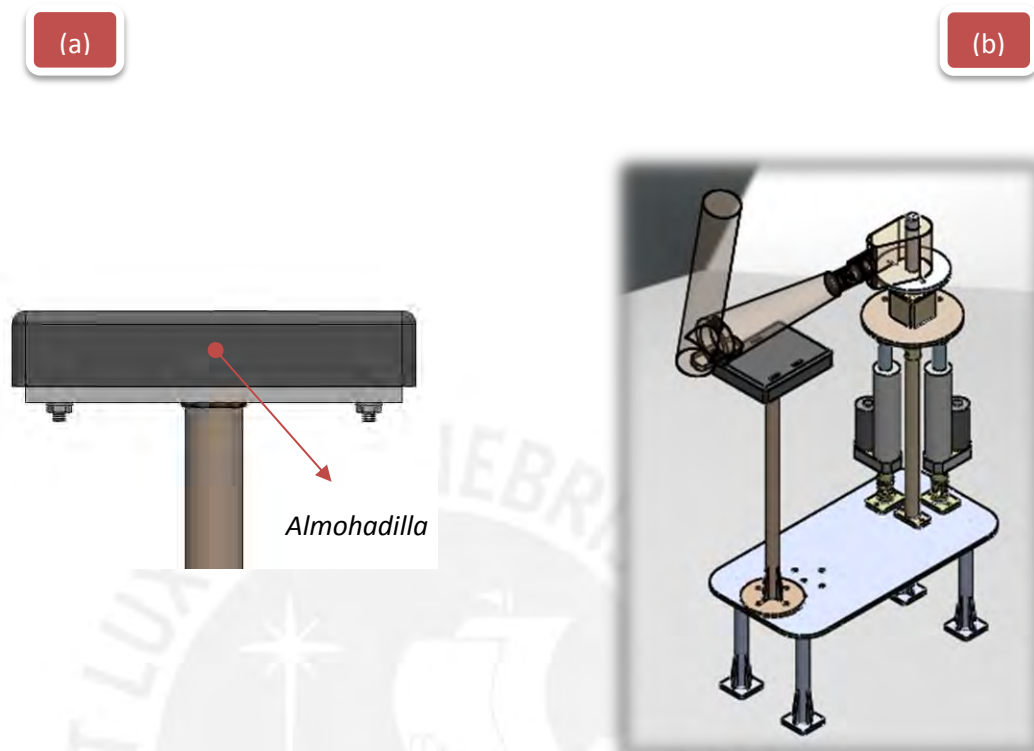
(a) Ensamble del soporte brazo con almohadilla. (b) Ensamble general del sistema.
